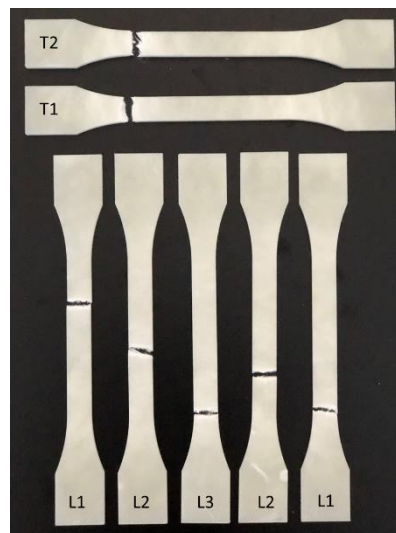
Lieu de rupture de différentes éprouvettes issues de la plaque B (dimensions Figure 3.19).
